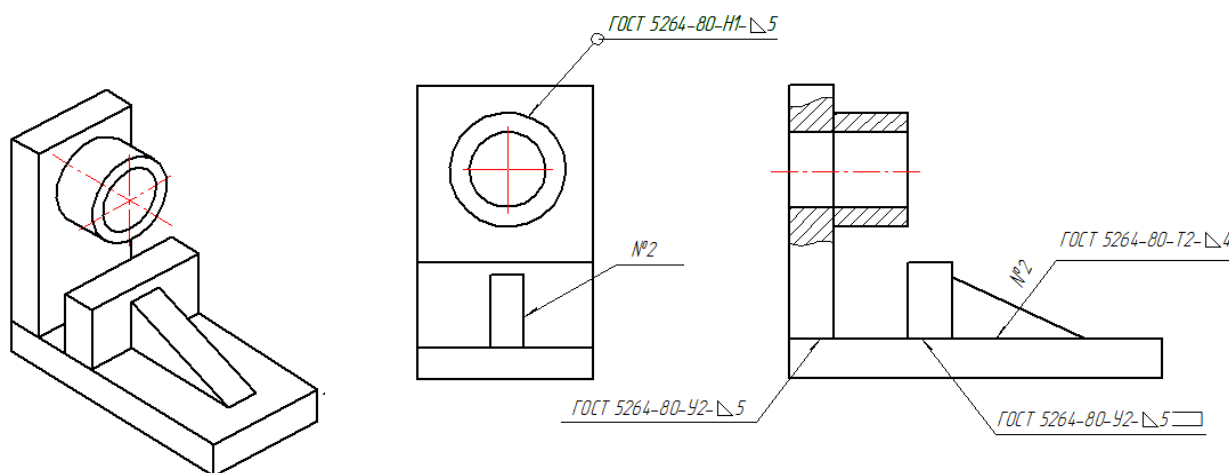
Пример выполнения чертежа сварного соединения (все сварные швы на чертеже различаются)
